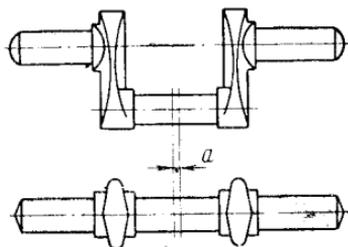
Поковка из двух кривошипов, выполненная в виде коленчатого вала:
